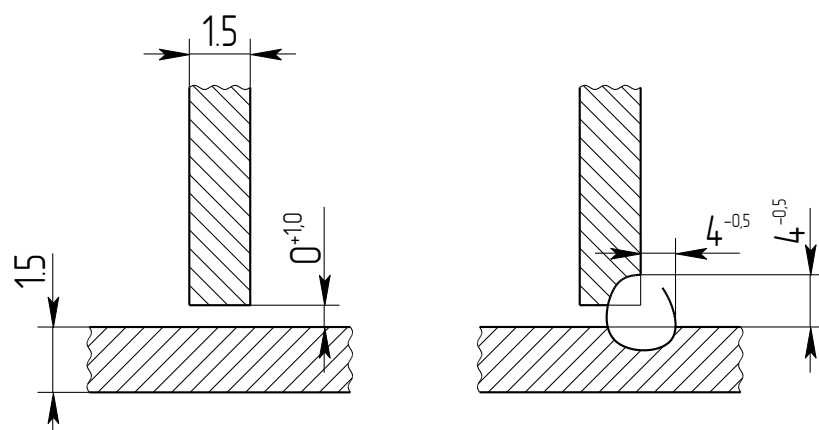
Конструктивные элементы сварного соединения Т1
